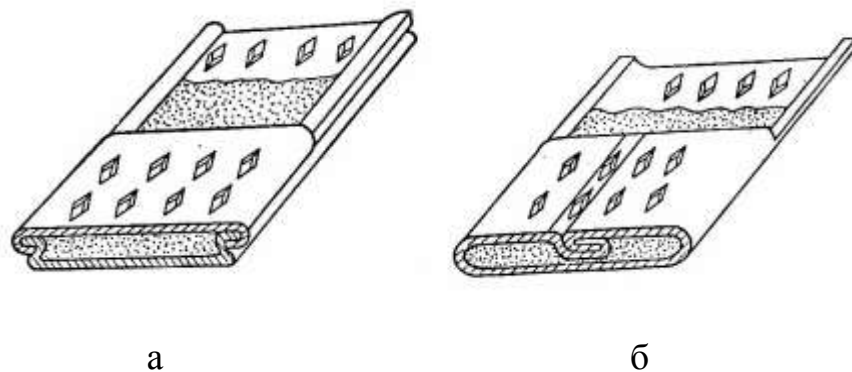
Конструкції порошкових стрічок: а - двозамкова; б - однозамкова
